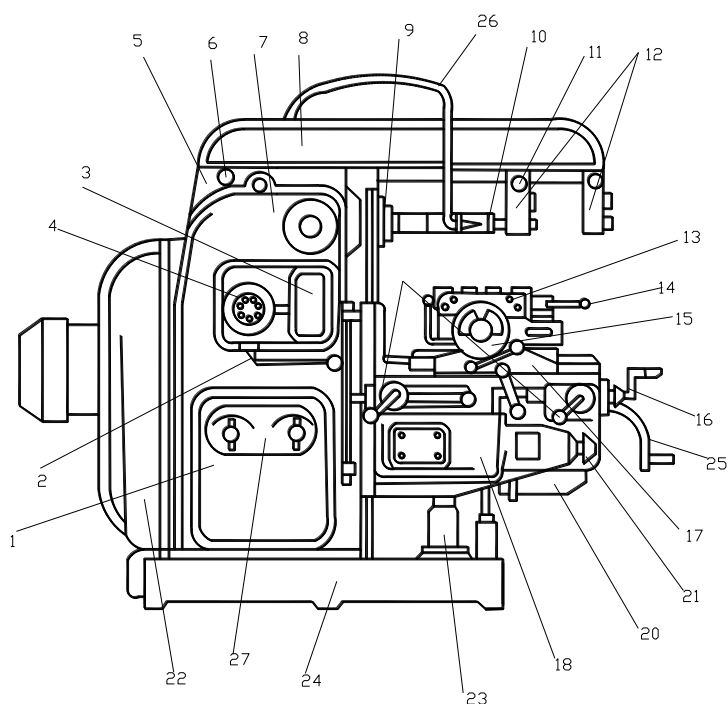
Схема устройства фрезерного станка типа 6P82Г
